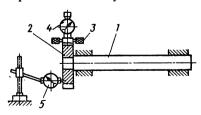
Схема проверки зубчатого колеса на радиальное и торцовое биения:
